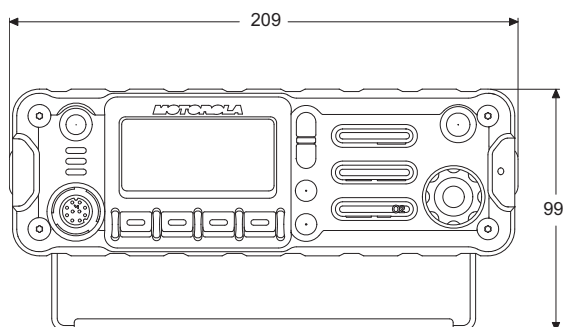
Vista Frontal da Cabeça de Controle O2 com Munhão e Montagem Remota
